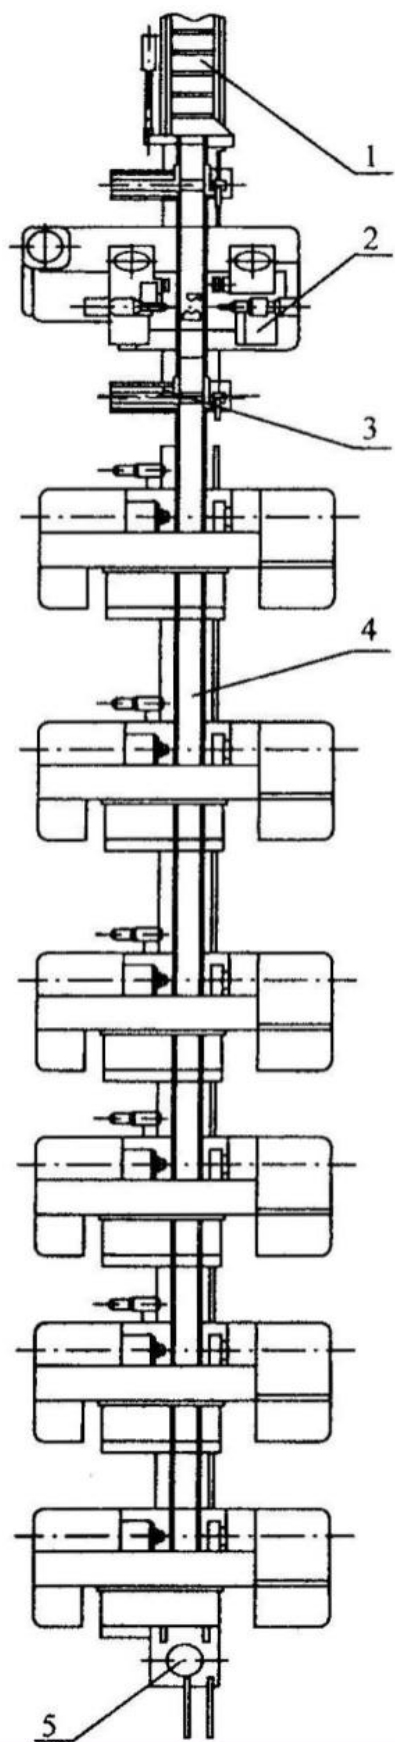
Схема автоматичної лінії для обробки валів
